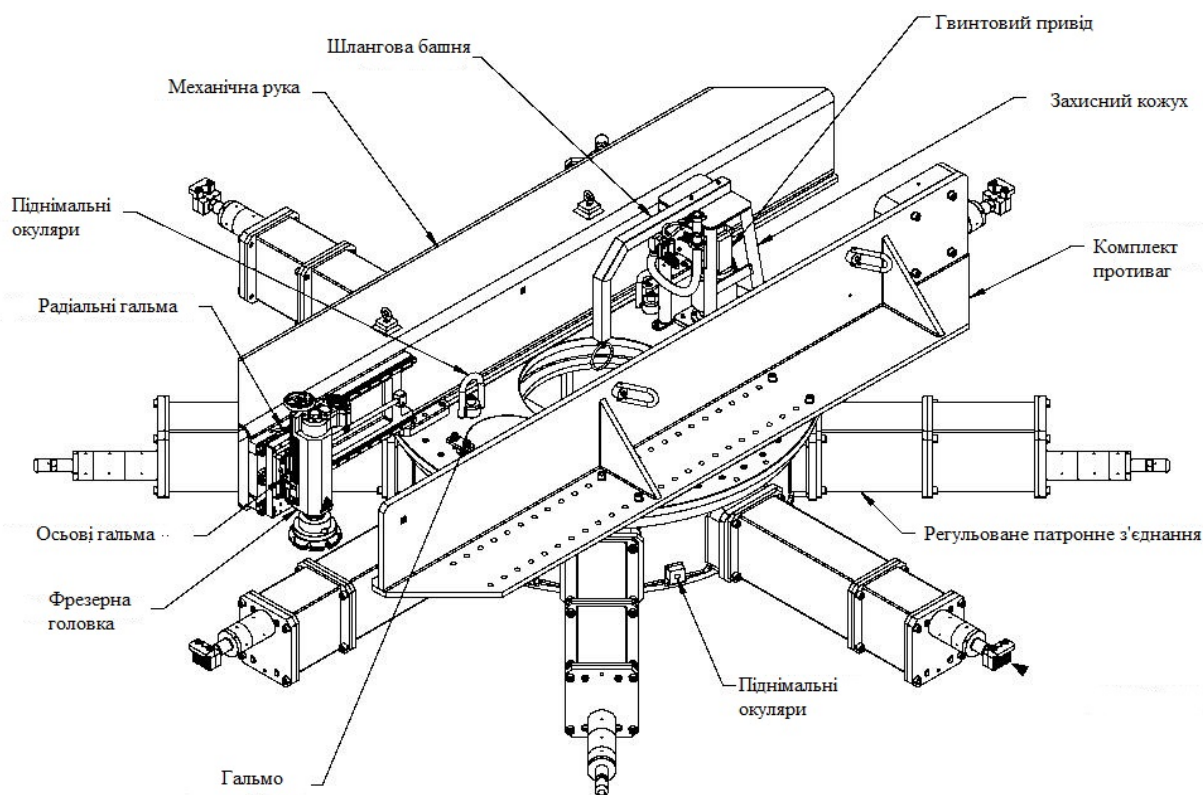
Карусельний фрезерний верстат SM6200
